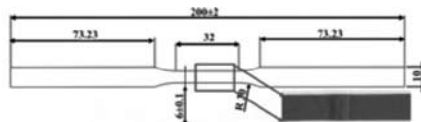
Geometría y dimensiones de la probeta de tracción.
